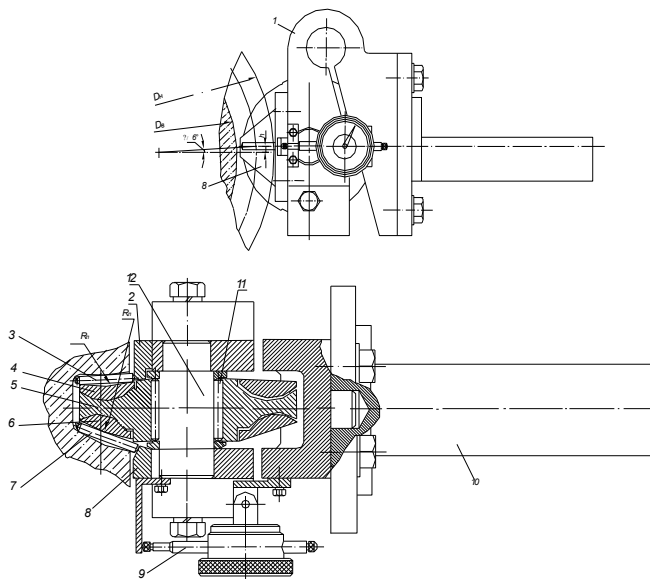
Схема устройства для обкатывания игольчатыми роликами упорной резьбы с шагом 64 мм
